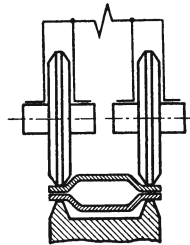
Gleichzeitiges Schweißen zweier Nähte.
